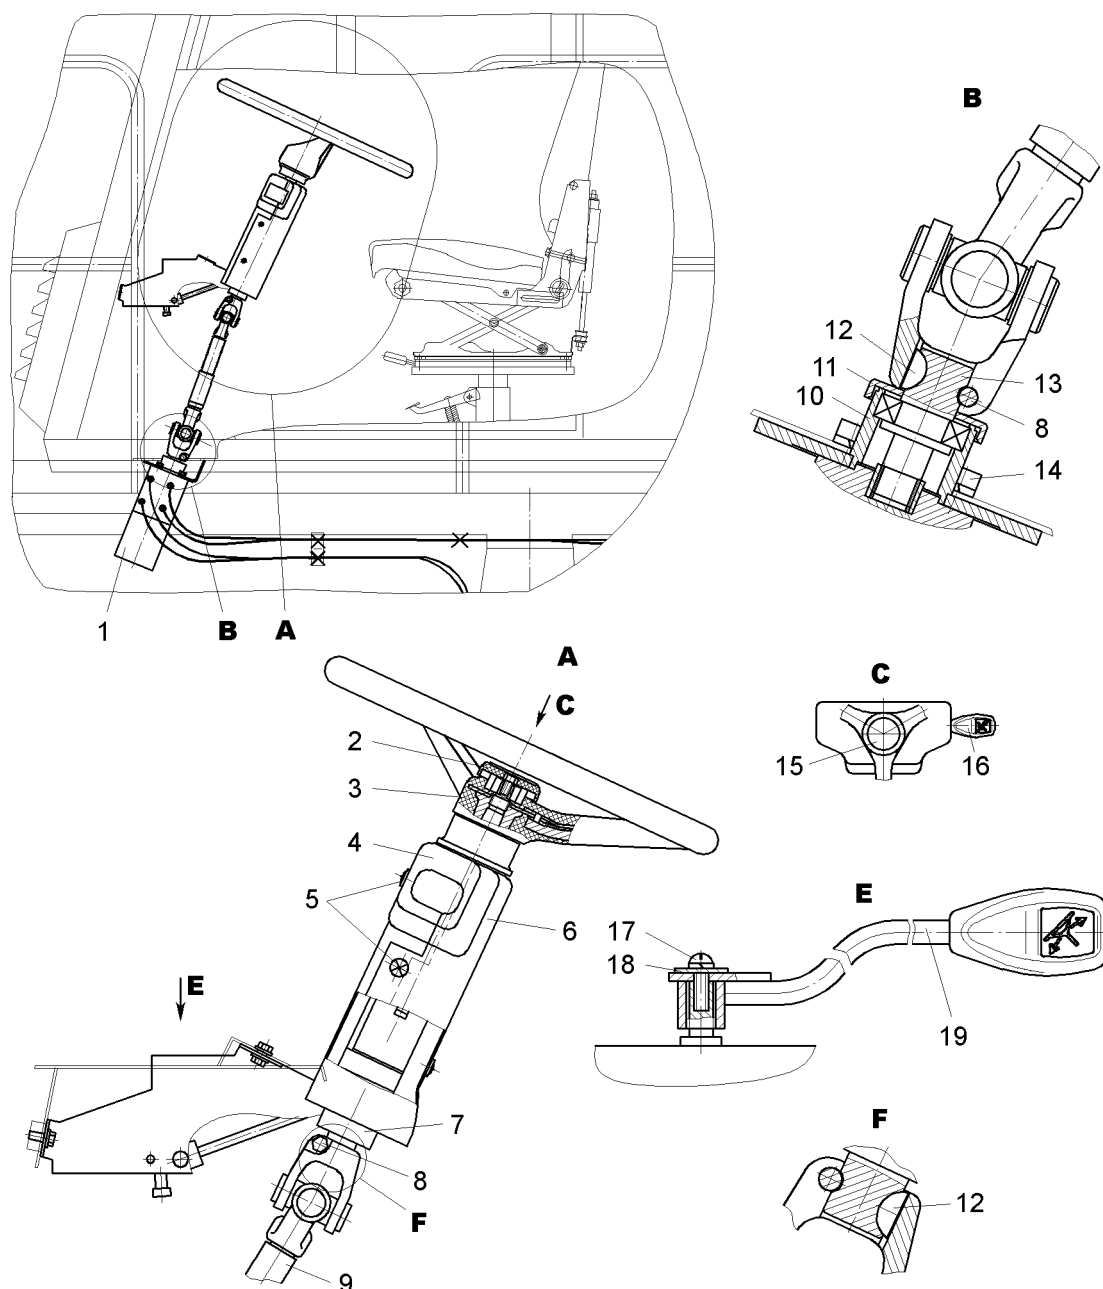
Механический привод гидравлического рулевого механизма:
